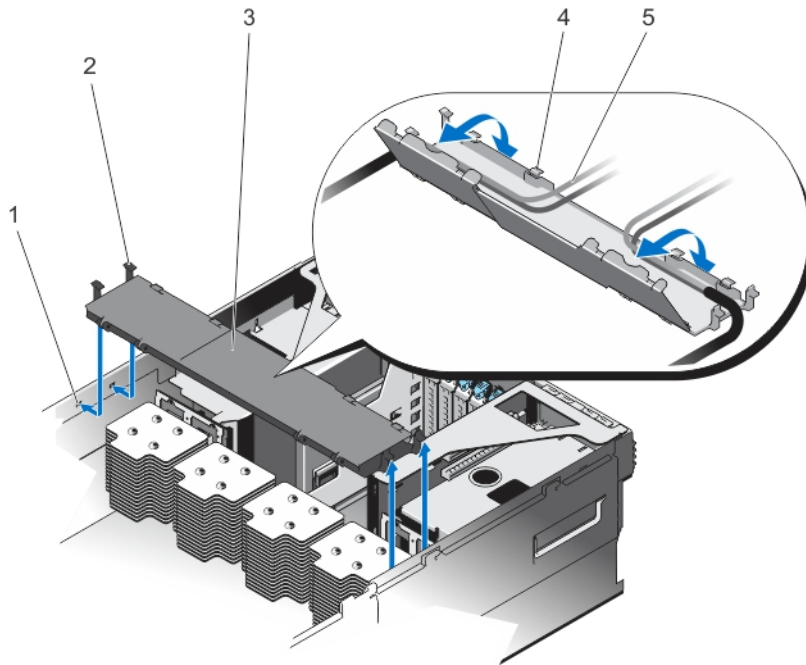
Extracción e instalación de la bandeja para tendido de cables
